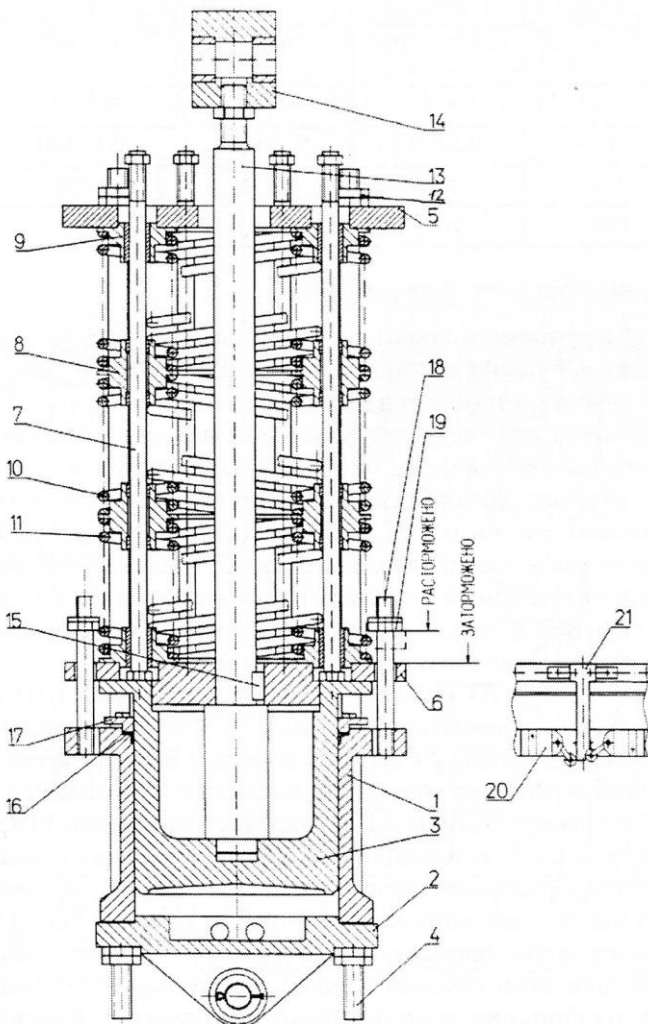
Пружинно-пневматичний привод гальма підйомних машин типу МПБ
